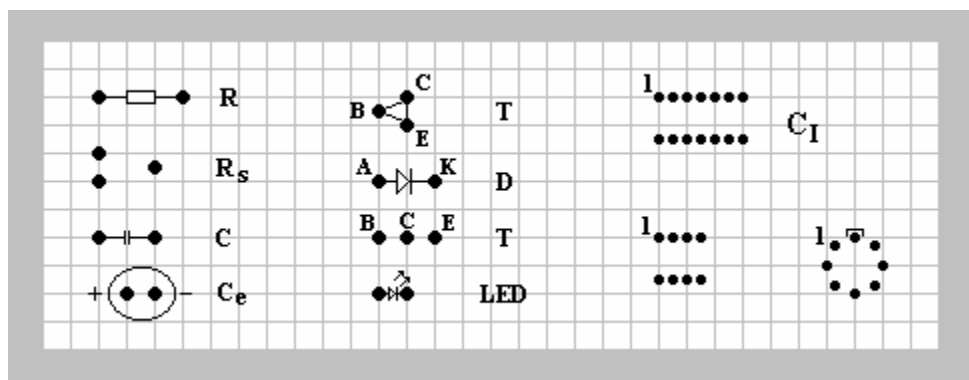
Dimensiuni folosite în realizarea desenului de cablaj.
